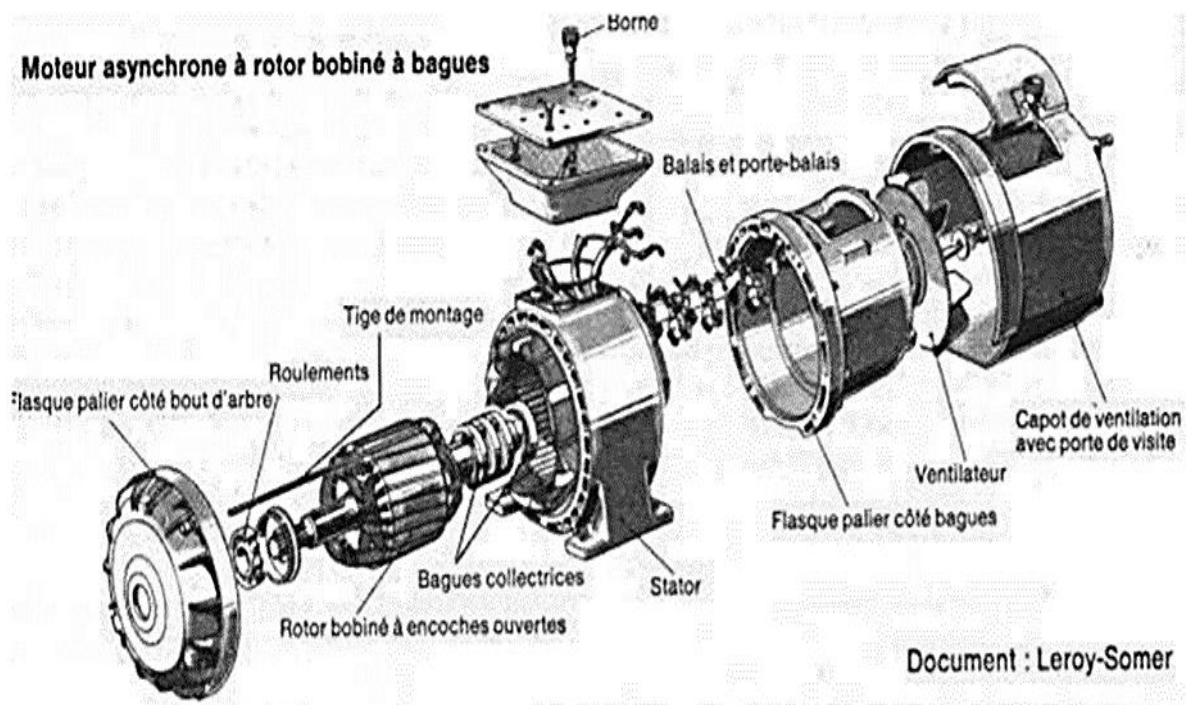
Moteur asynchrone à rotor bobiné à bagues
